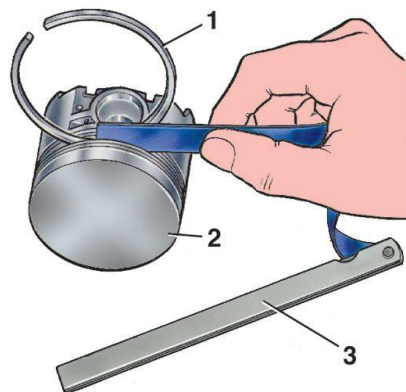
Проверка бокового зазора между кольцом и канавкой поршня: 1 – поршневое кольцо, 2 – поршень, 3 – набор щупов
